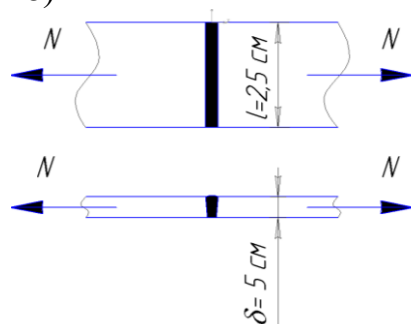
Схема действия нагрузки на стыковой сварной шов
